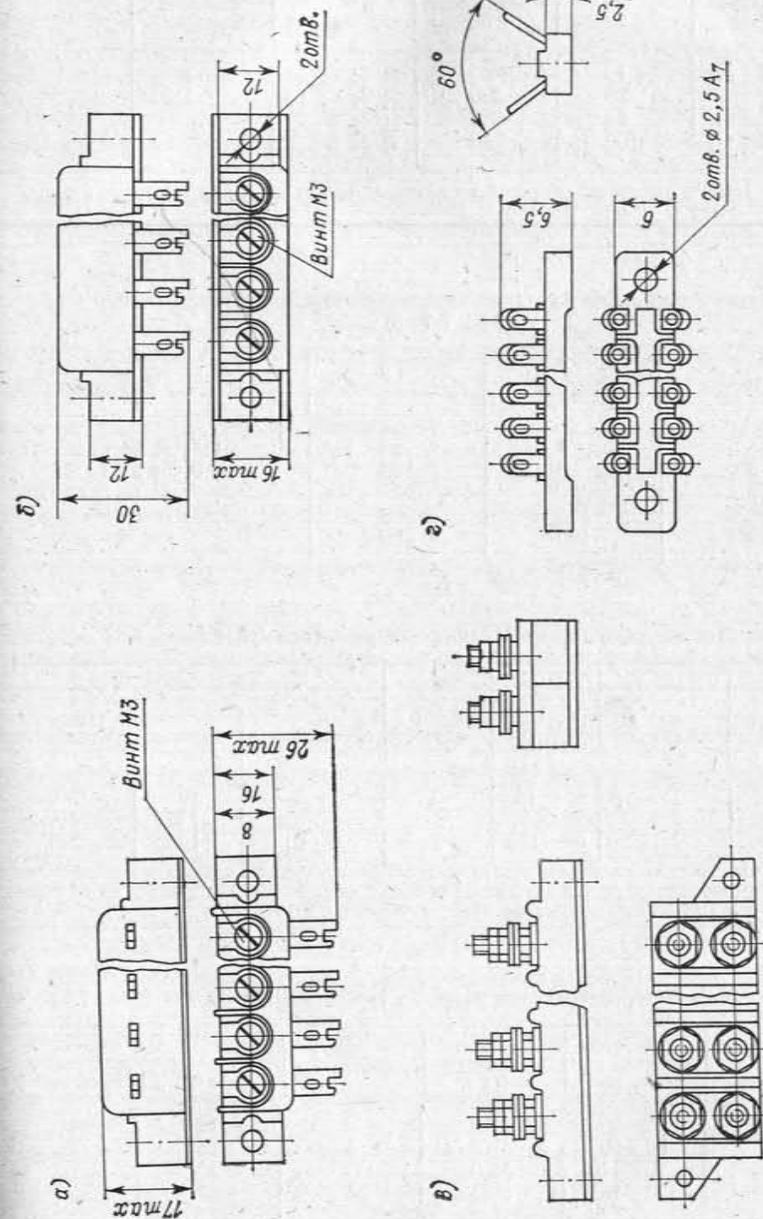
Платы соединительные: а — типа ПС3; б — типа ПС4; в — типов ПС5 — ПС9; г — типа ПС11.
